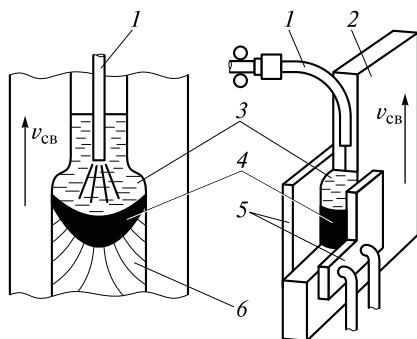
Схема процесса электрошлаковой сварки:
